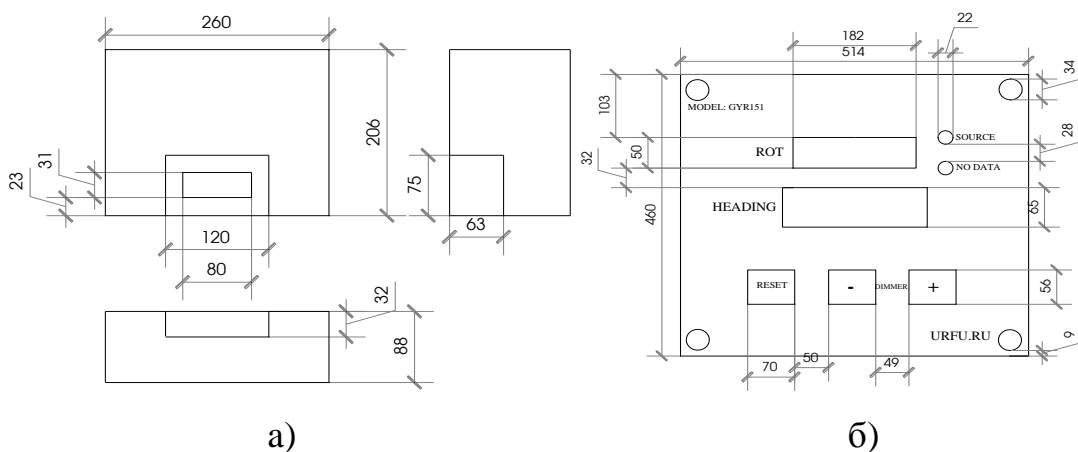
Чертежи корпуса цифрового устройства отображения
